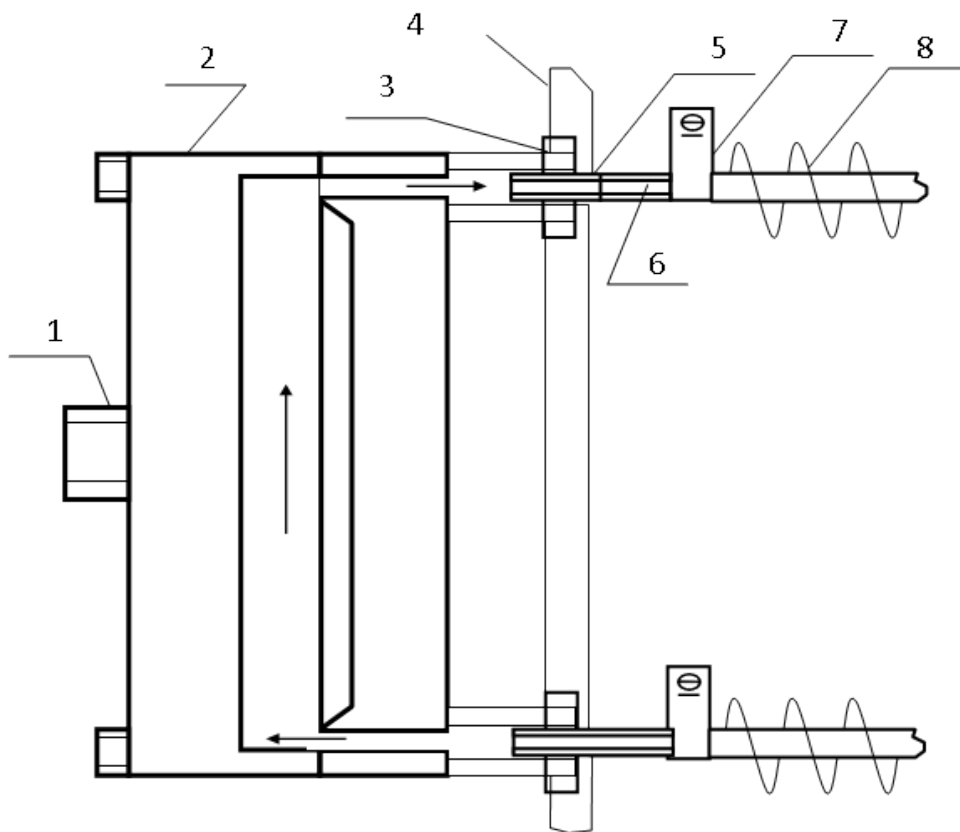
Схема з'єднання кварцевих трубок калачами в торцевій стінці камери ПЧ-електронагріву: 1 – стяжний гвинт; 2 – калач; 3 – гумова прокладка; 4 – торцева стінка камери; 5 – наконечник кварцової трубки; 6 – кварцева трубка; 7 – хомут для кріплення спіралі; 8 – спіраль.
